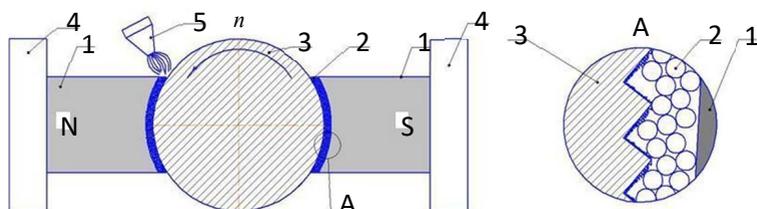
Схема магнито-абразивной обработки цилиндрической поверхности: 1 – сердечники; 2 – ферромагнитный порошок; 3 – деталь; 4 – держатели; 5 – сопло для подачи рабочей жидкости
